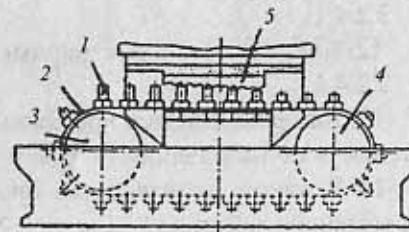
Схема обработки на протяжном станке непрерывного действия:
